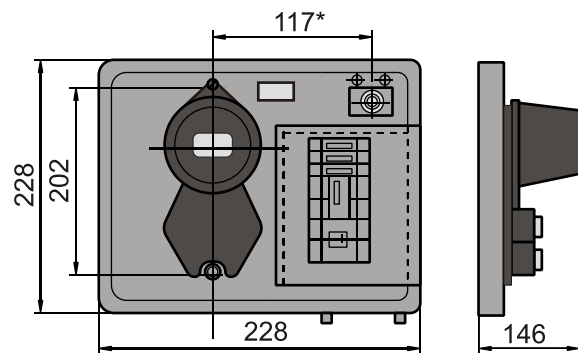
Внешний вид и габаритные размеры ЩК1109-02
